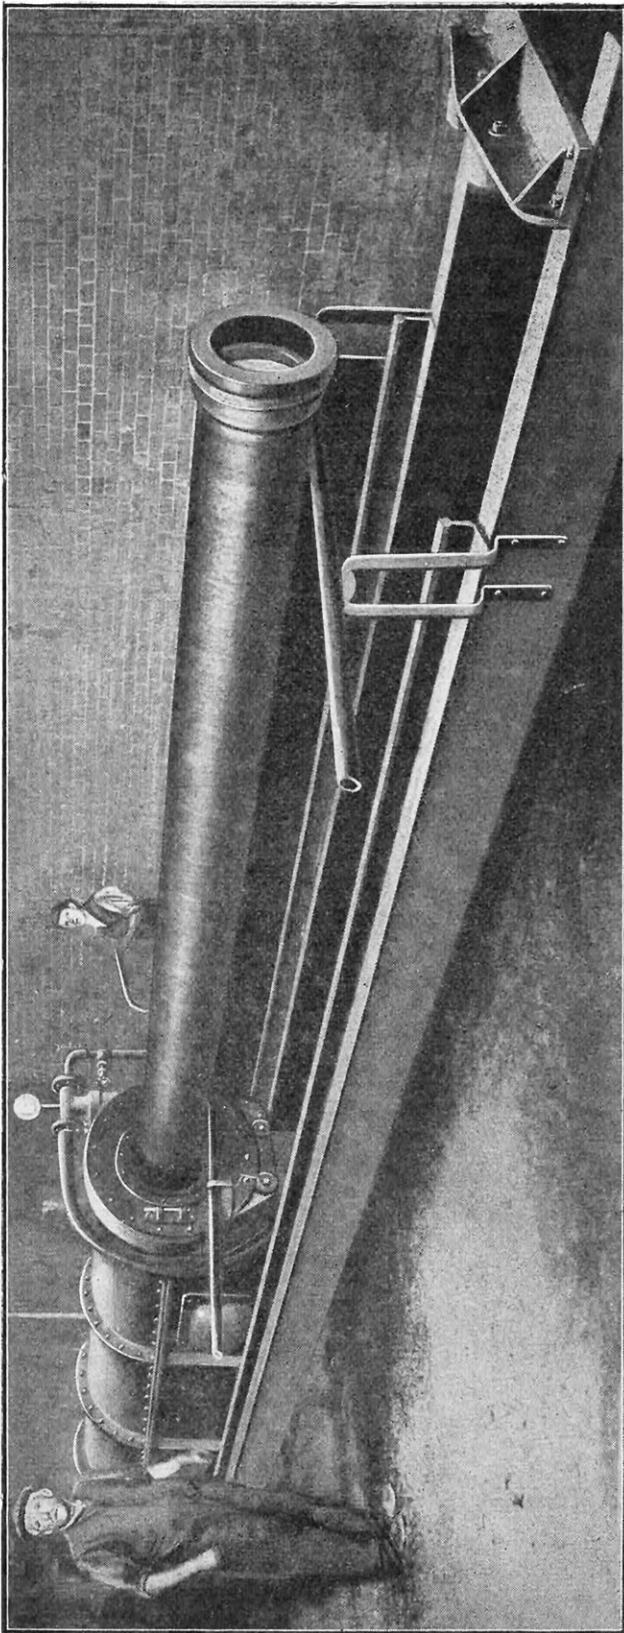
TUYAU DE FONTE DE GRANDES DIMENSIONS TEL QU'IL APPARAÎT IMMÉDIATEMENT APRÈS SA SORTIE DU MOULE
